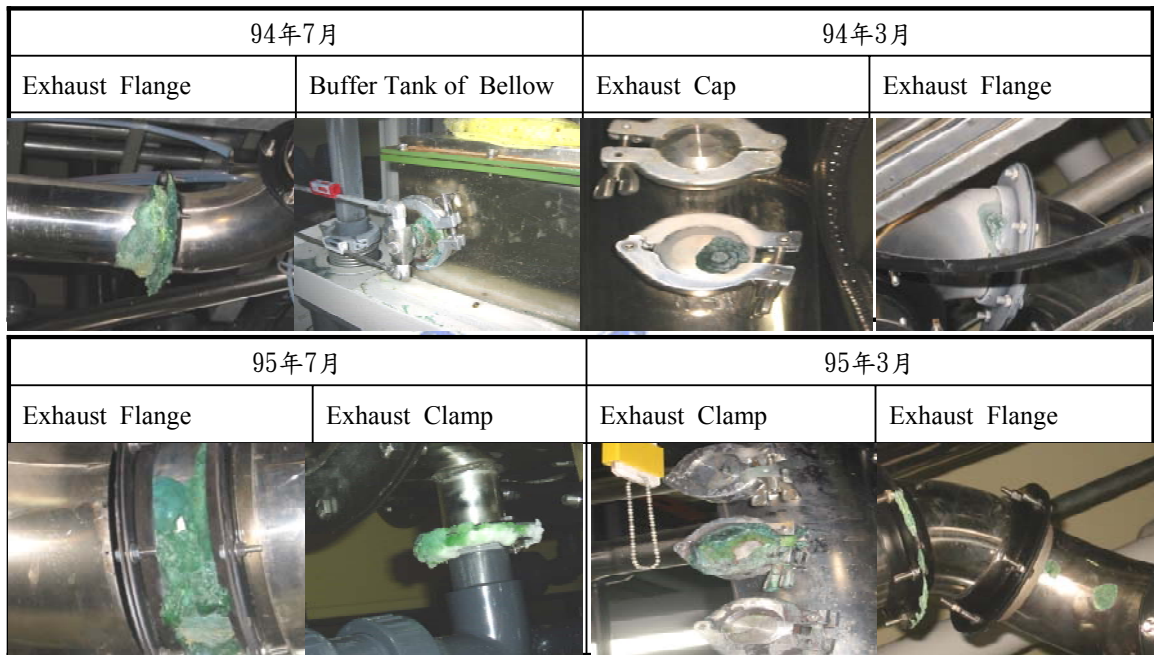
Exhaust Flange 及 Clamp 結晶腐蝕狀況
